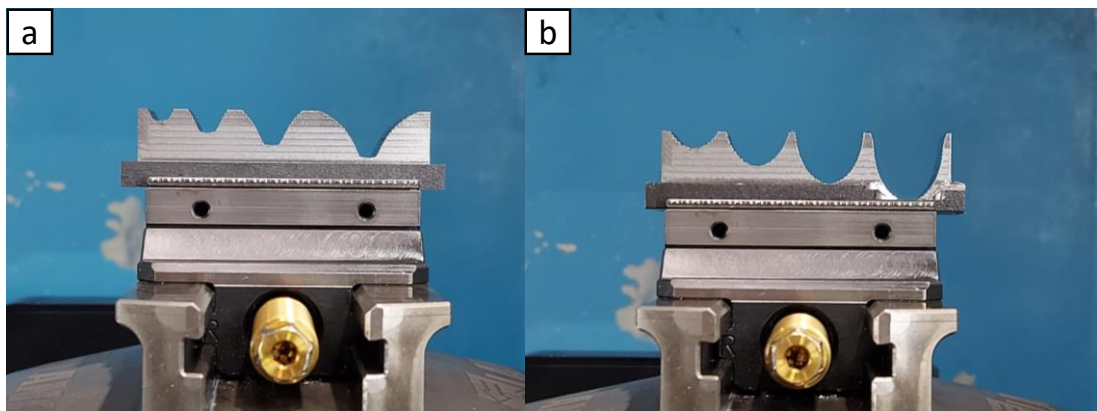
Probetas de ensayos de caracterización de coeficientes de corte: a) Probeta del compresor de tornillo sin fin simétrico macho y b) Probeta del compresor de tornillo sin fin simétrico hembra.
